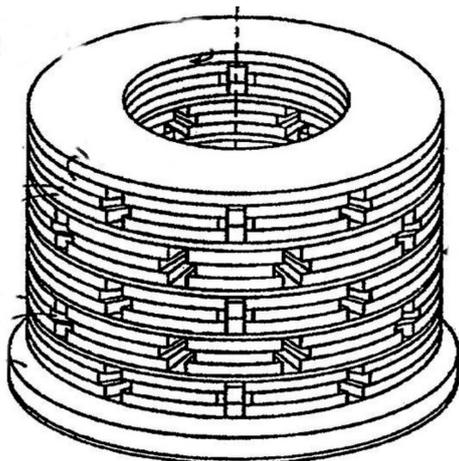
Схема дроссельной насадки с отверстиями в виде креста
